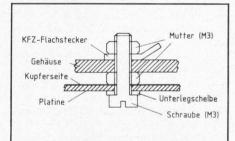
Schnittzeichnung zur Verbindung von Platine, Gehäuseoberteil und Kfz-Flachstecker mittels Schrauben und Muttern M 3
